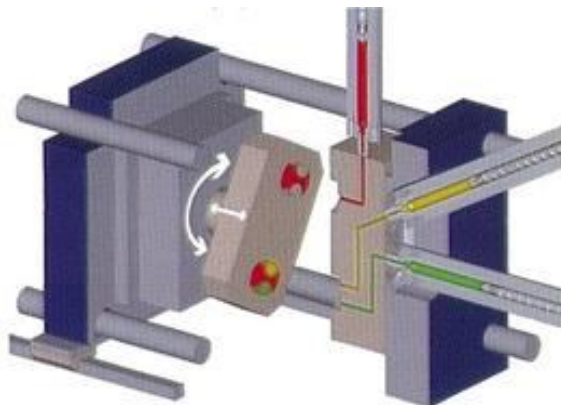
Princip překládání výrobků pomocí rotace formy [7]
